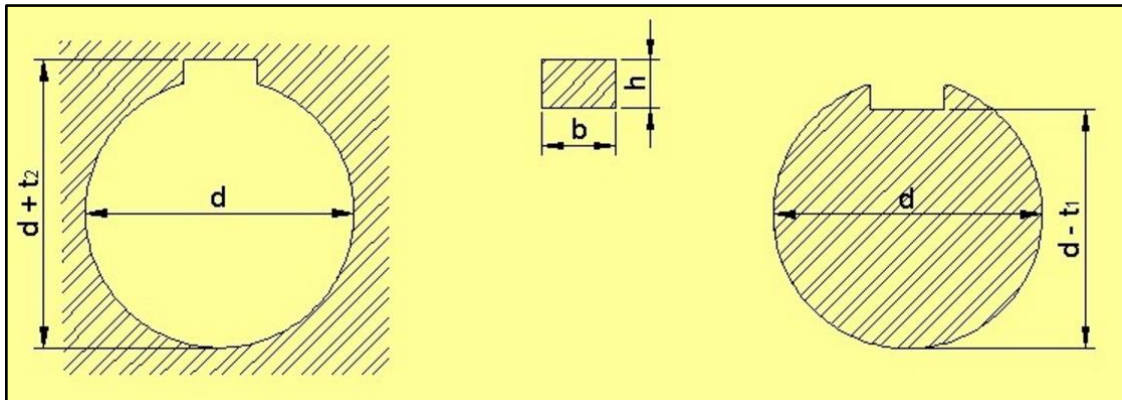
Desenho esquemáticos das dimensões de chavetas de perfil paralelo
